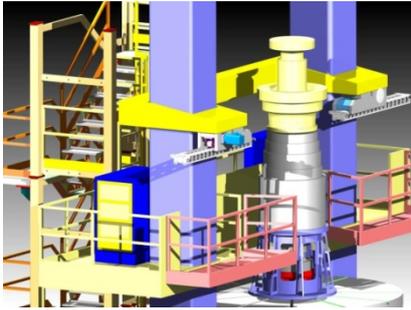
Mit zwei WIG-Heißdraht-Engspaltbrennern ausgestattete Schweißstation zum Fügen von Turbinenrädern.
